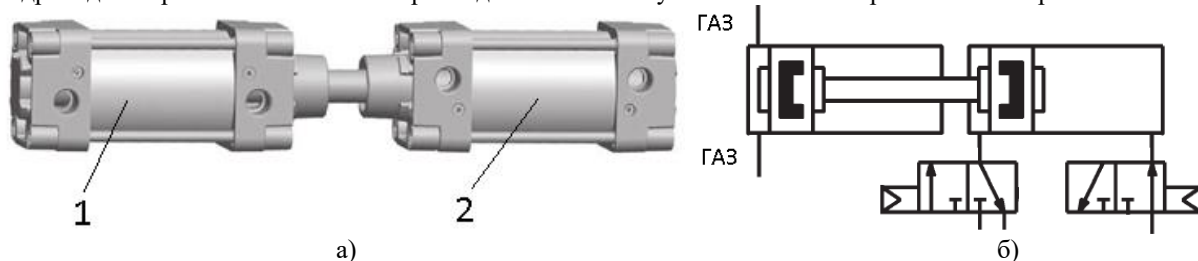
Типовий опозитний пневмоциліндр (а) та пневматична схема циліндра – дозатора (б)
